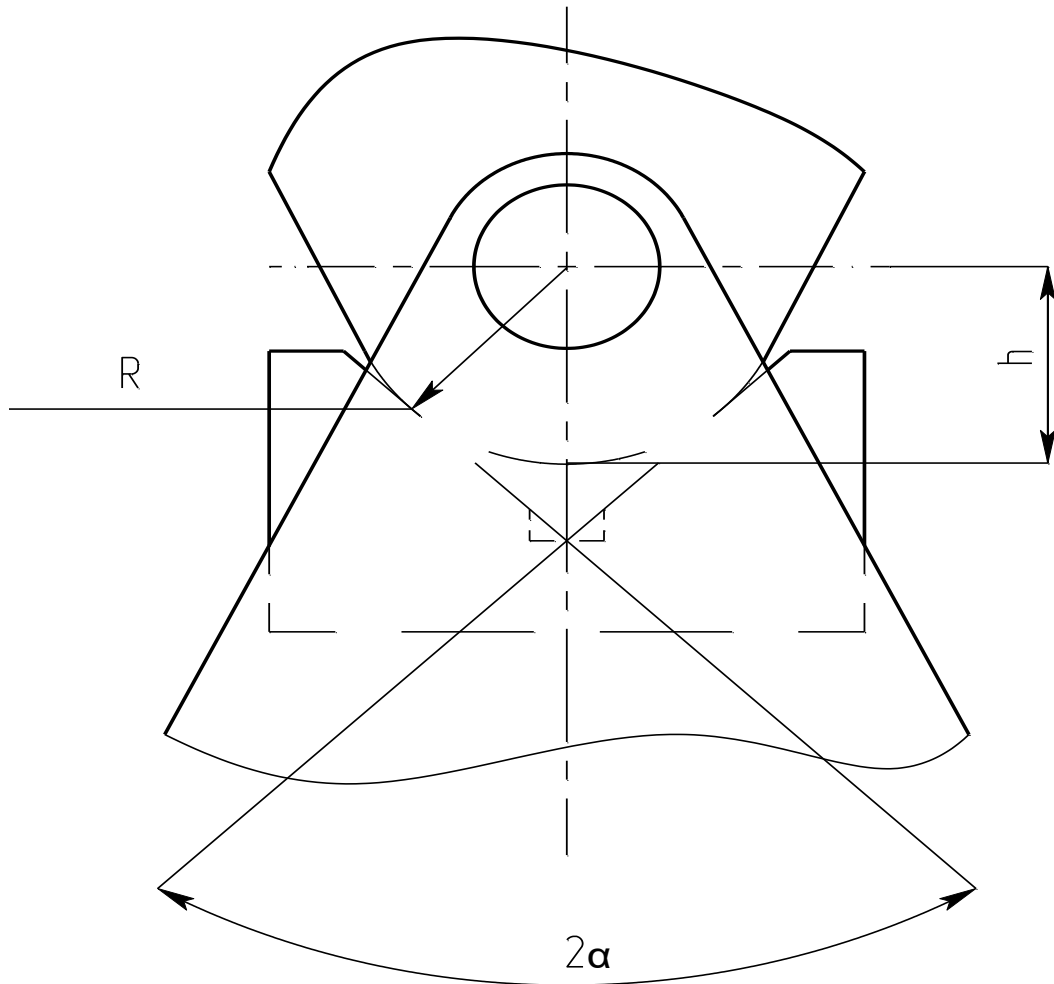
Схема базування деталі в призмі при свердлінні в кондукторі
